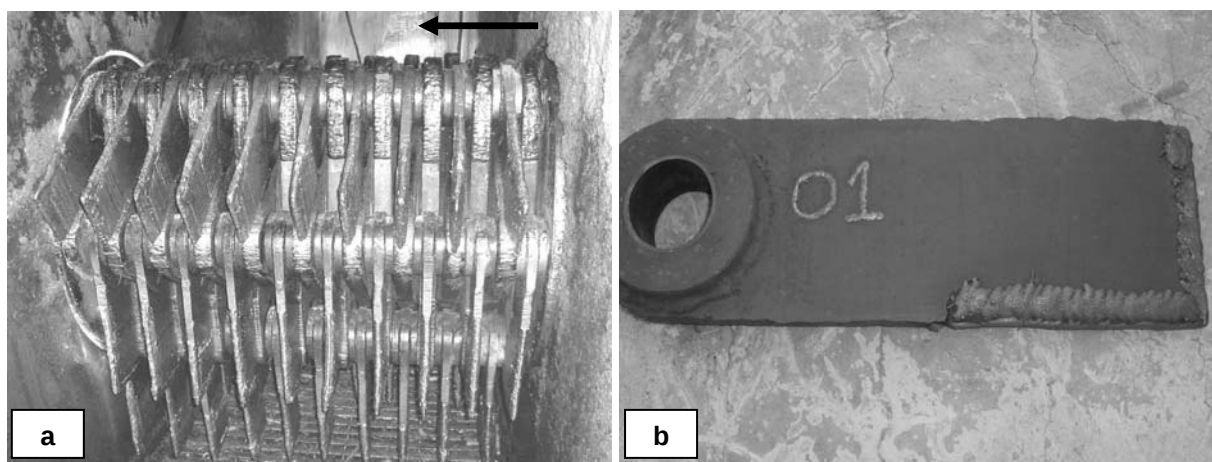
Vista interna do picador (a) e detalhe de uma faca picadora (b).
